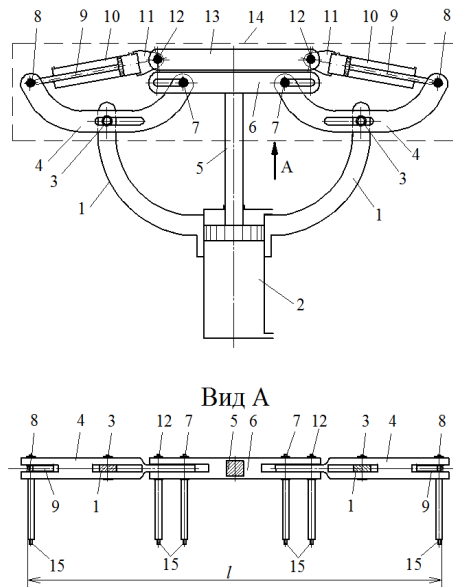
Рычажно-шарнирное захватное устройство в закрытом положении
